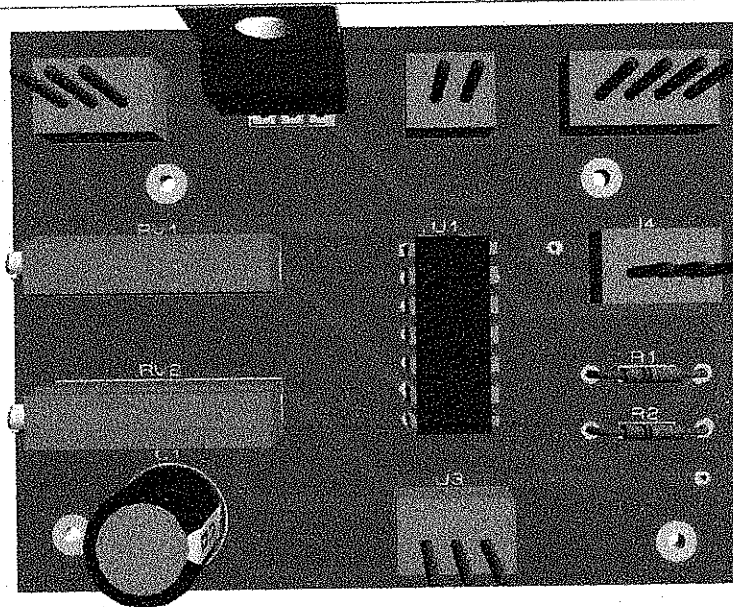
Tarjeta de acondicionamiento vista en 3 dimensiones (3D)
